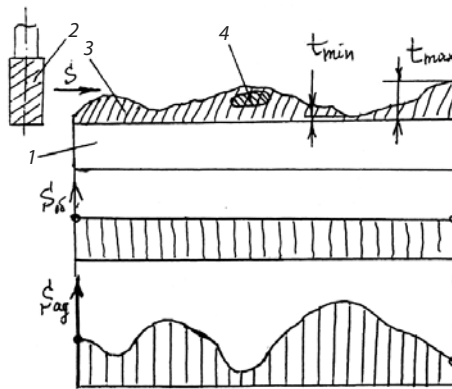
Пример обработки заготовки на фрезерном станке при обычном ($S_{об}$) и адаптивном ($S_{ад}$) управлении
